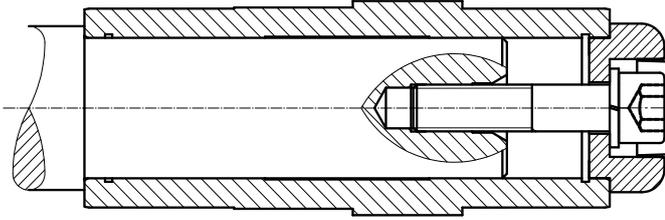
riduttore fissato ad un albero con spallamento mediante elemento di fissaggio
